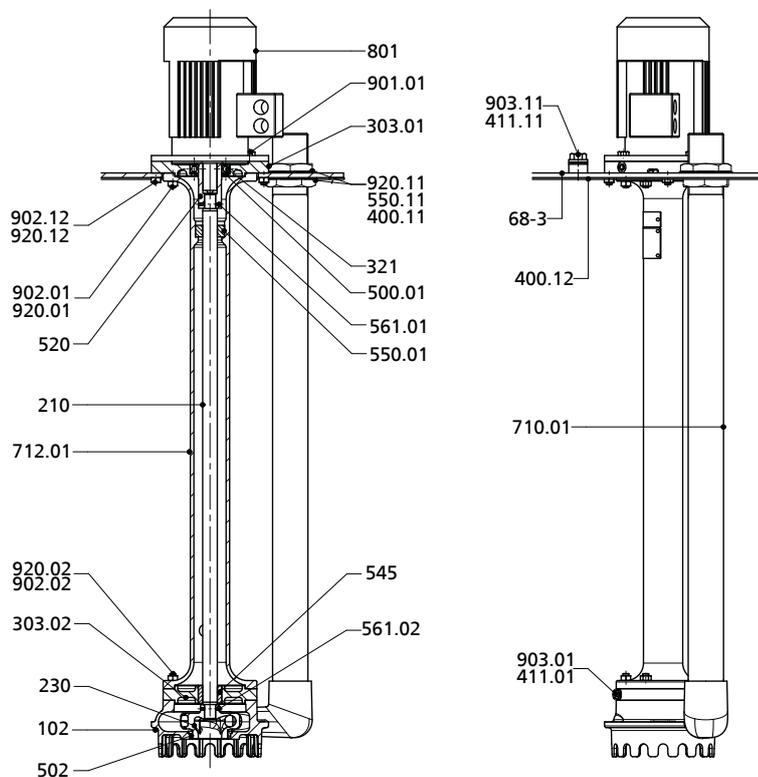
Чертеж МК, МКА - глубина установки 1000 мм
